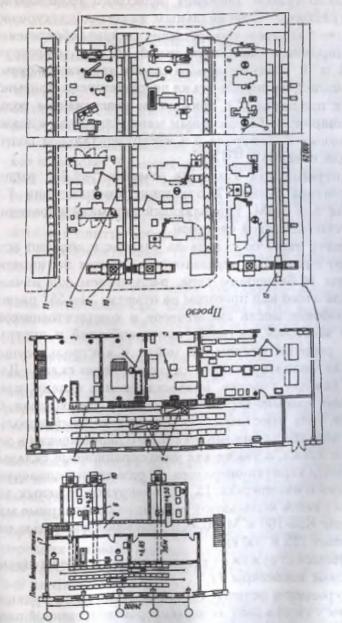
Планировка оборудования и рабочих мест сборочного цеха шлифовальных станков:
